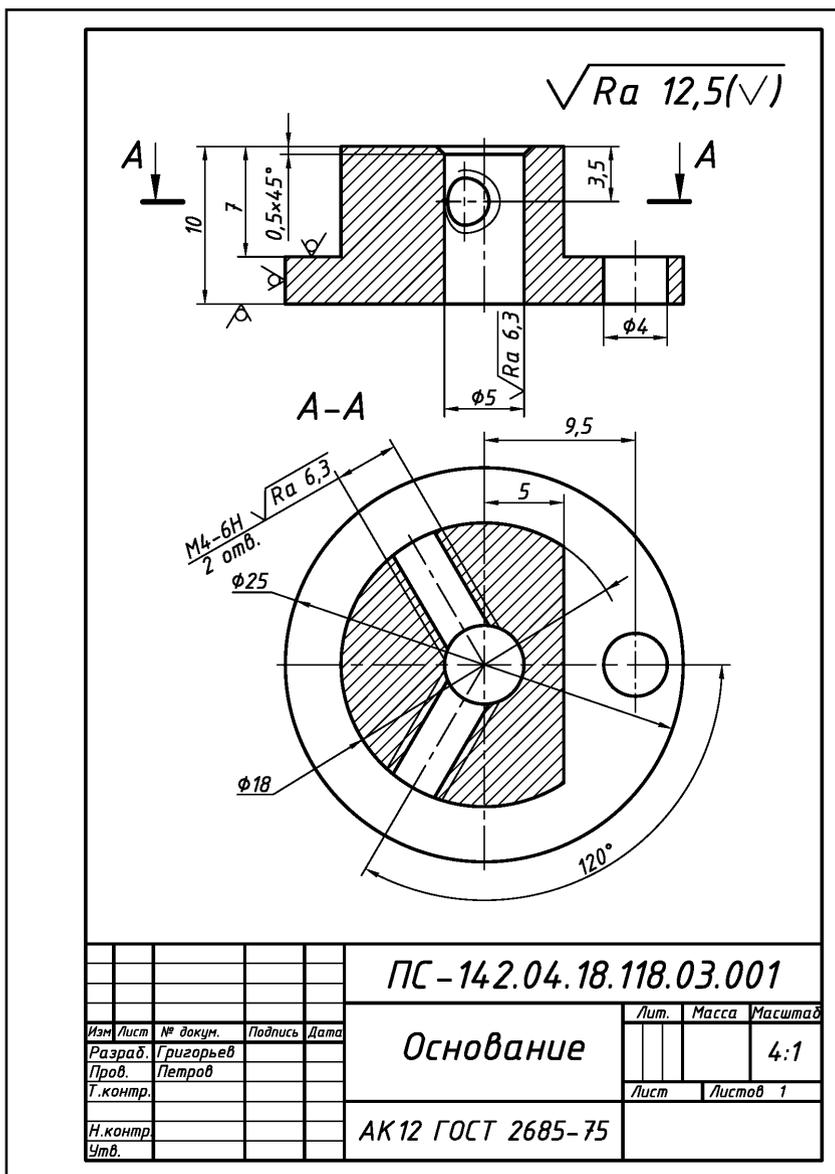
Оформление рабочего чертежа детали «Основание» сборочной единицы «Корпус» (рис. 1.72)
